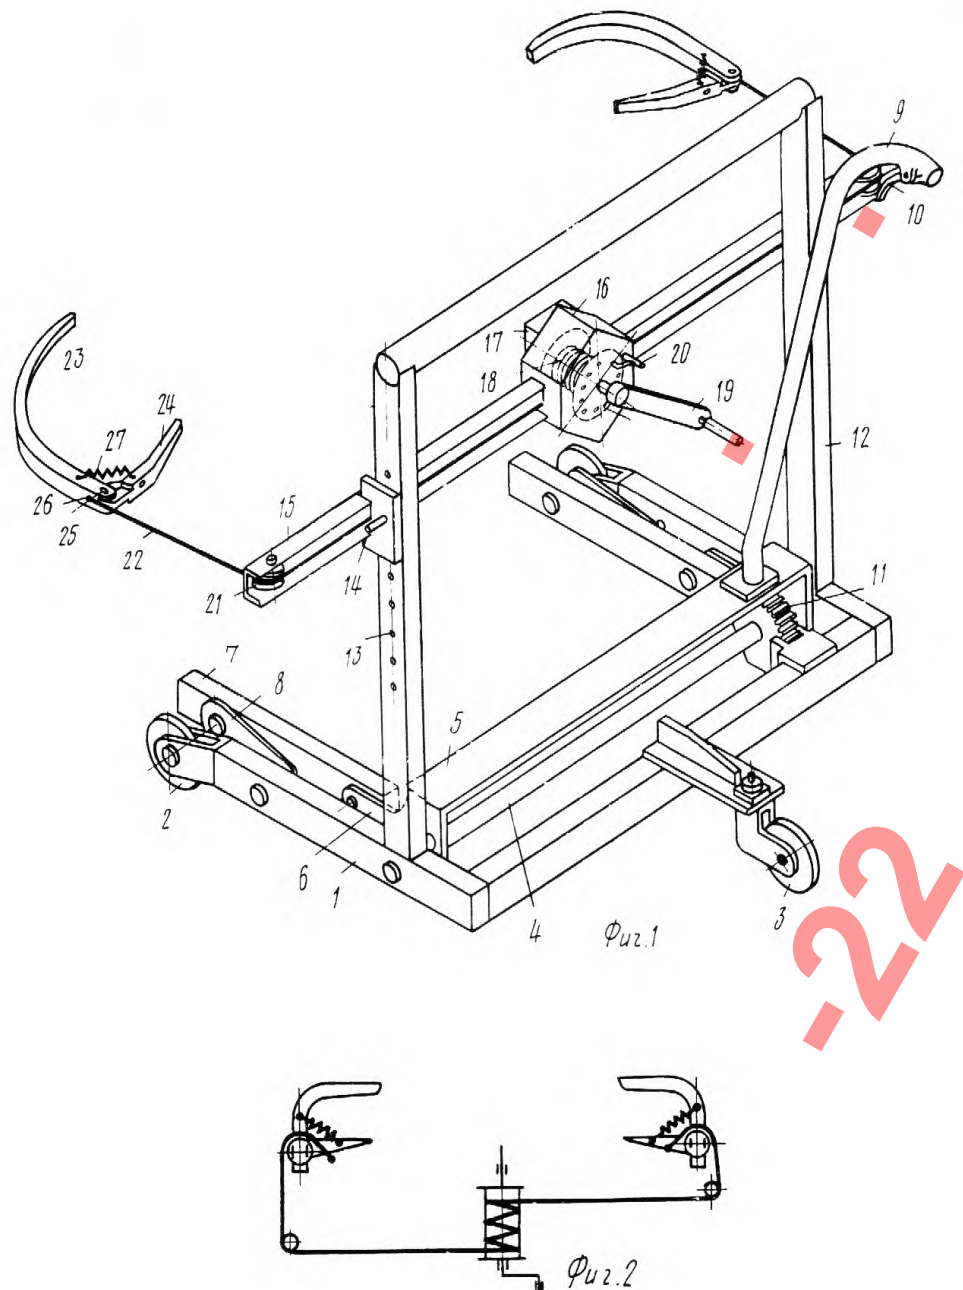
Візок зі знімачем для заміни коліс транспортних засобів (Авторське свідоцтво № 897593): 1 – основа; 2 – колеса неповоротні; 3 – колесо поворотне; 4 – вал; 5 – траверса; 6 – важелі; 7 – лижі підйому; 8 – важіль пасивний; 9 – ручка підйому; 10 – ручка управління засувкою; 11 – зубчастий сектор; 12 – рама П-подібна; 13 – отвори; 14 – пальці-фіксатори; 15 – балка знімача; 16 – корпус лебідки-знімача; 17 – упор; 18 – тросовий барабан; 19 – приводна ручка; 20 – фіксатор; 21 – обвідні ролики; 22 – трос; 23 – захватні скоби; 24 – затискний важіль; 25 – палець; 26 – вікно; 27 – пружина.
